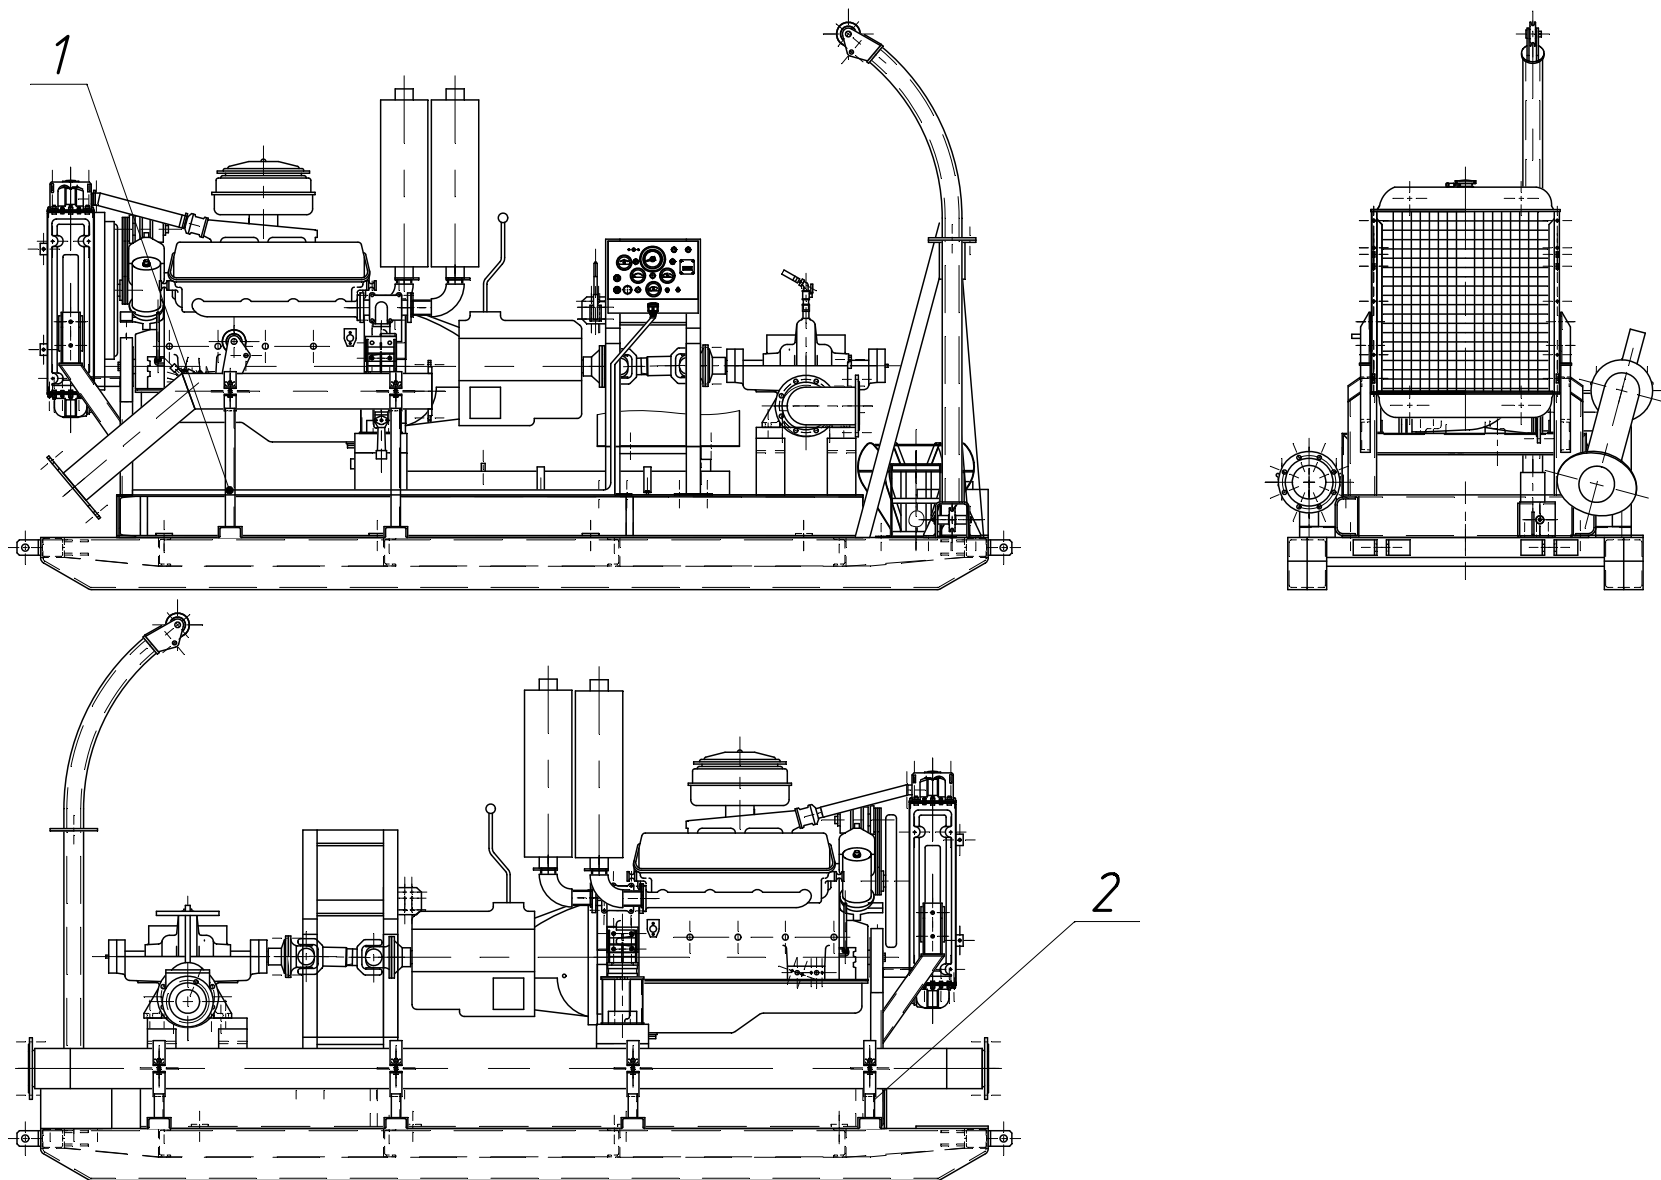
Общий вид агрегатов типа ДНА-п в транспортном положении
